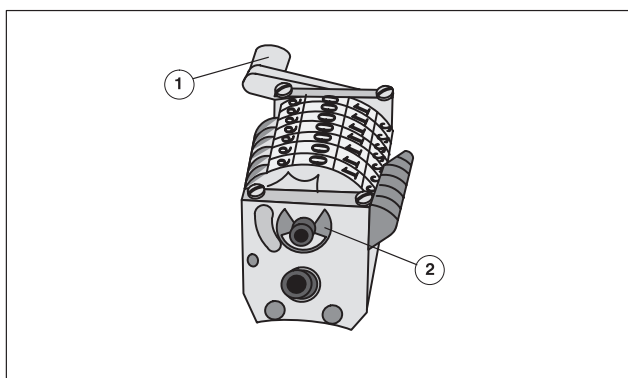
Продольный нумератор, перестановка рукоятки переключения на другую сторону нумератора
